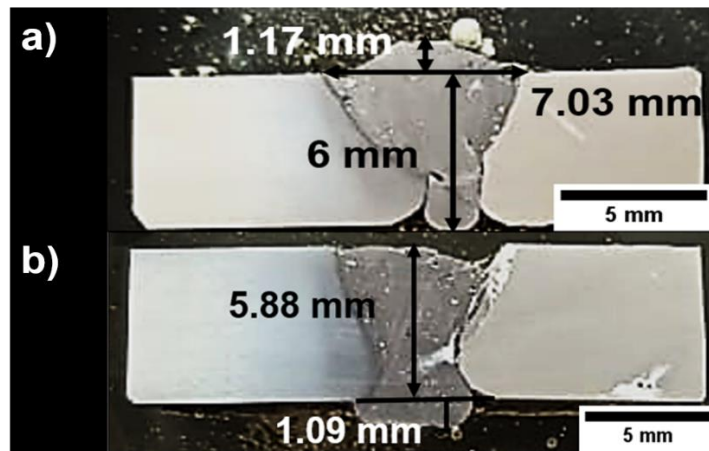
90 Unión de las placas de aleación de aluminio a) Soldadura 33 y b) réplica de la soldadura 33.
